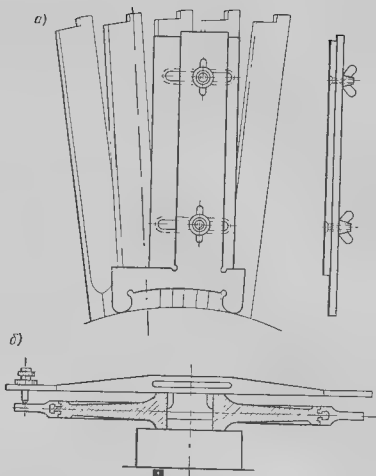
Проверка положения лопаток на колесе: а — радиальной; б — аксиального
